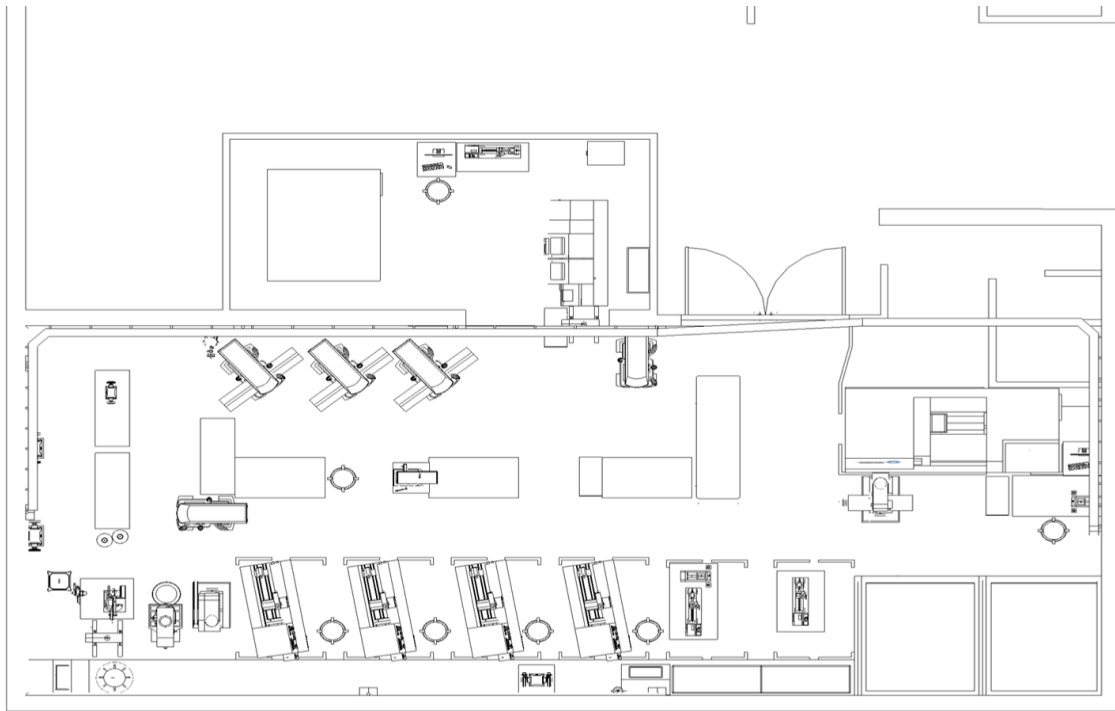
Lay Out actual de la empresa RB. Fuente: Elaboración propia
